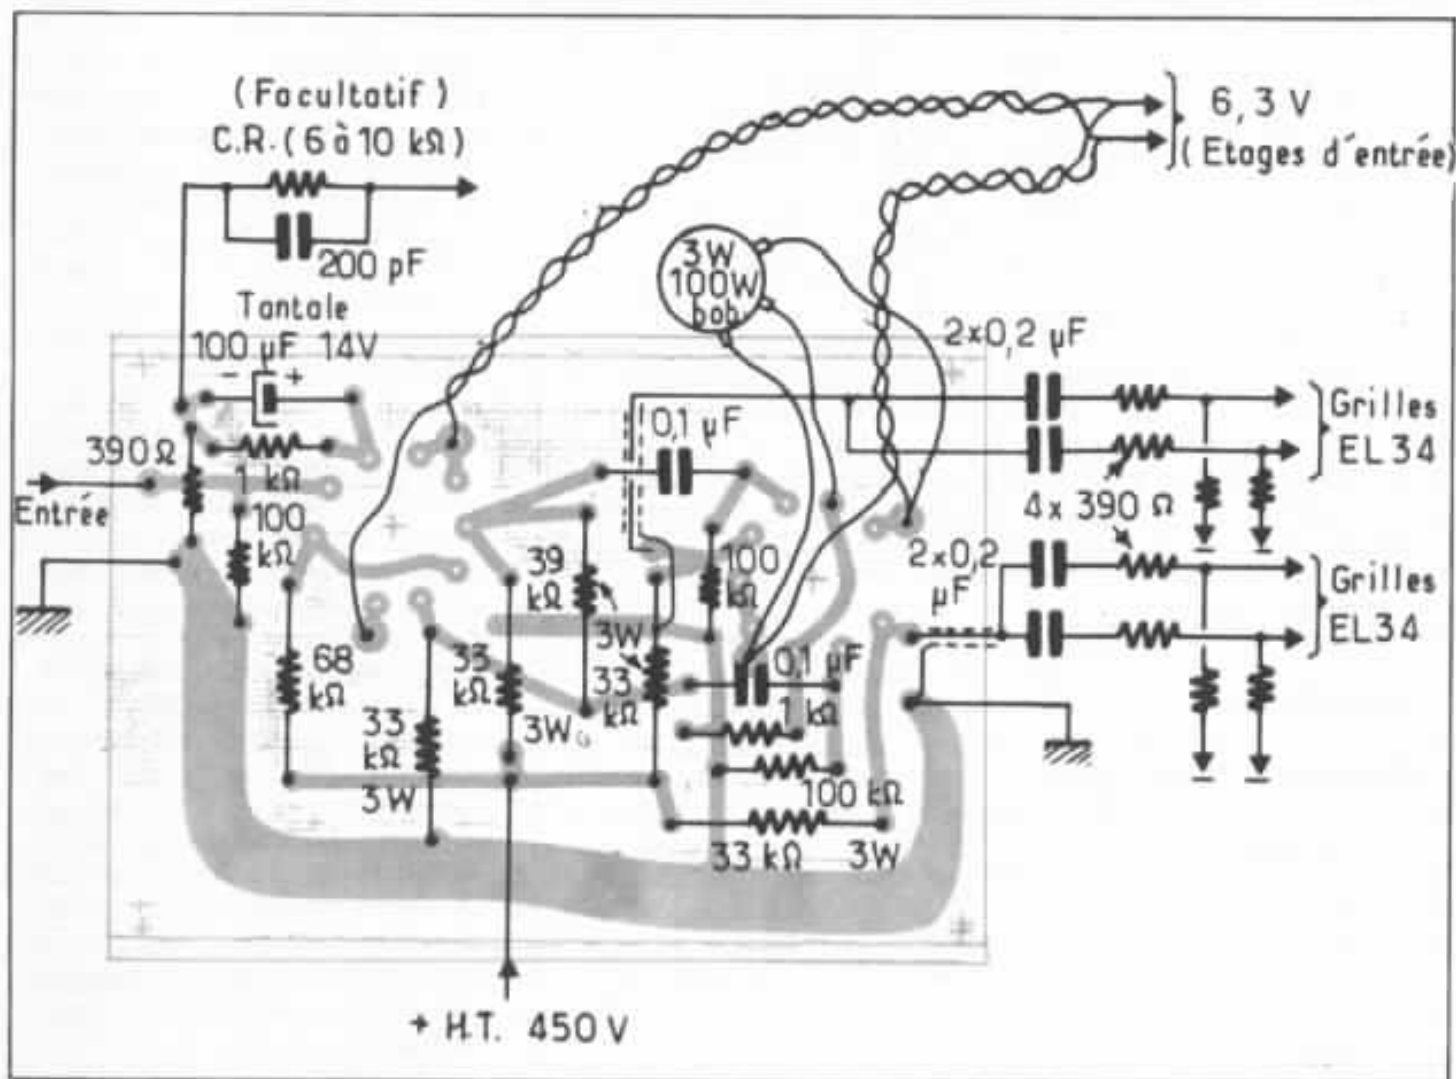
a. Circuit imprimé vu de dessous (côté soudure).
